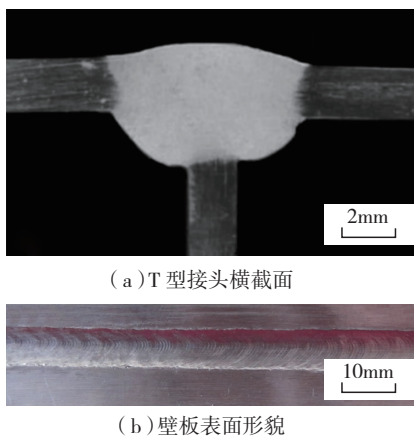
激光-电弧复合冷填丝焊接镁合金T型接头形貌
